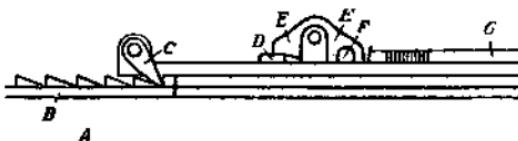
Детали механизма для натягивания гастрафета (вид сбоку). А—ложе арбалета, В—металлическая зубчатая планка, С—стопорные задержки, D—спуск, Е—затяжка, F—тетива, G—стрела.
